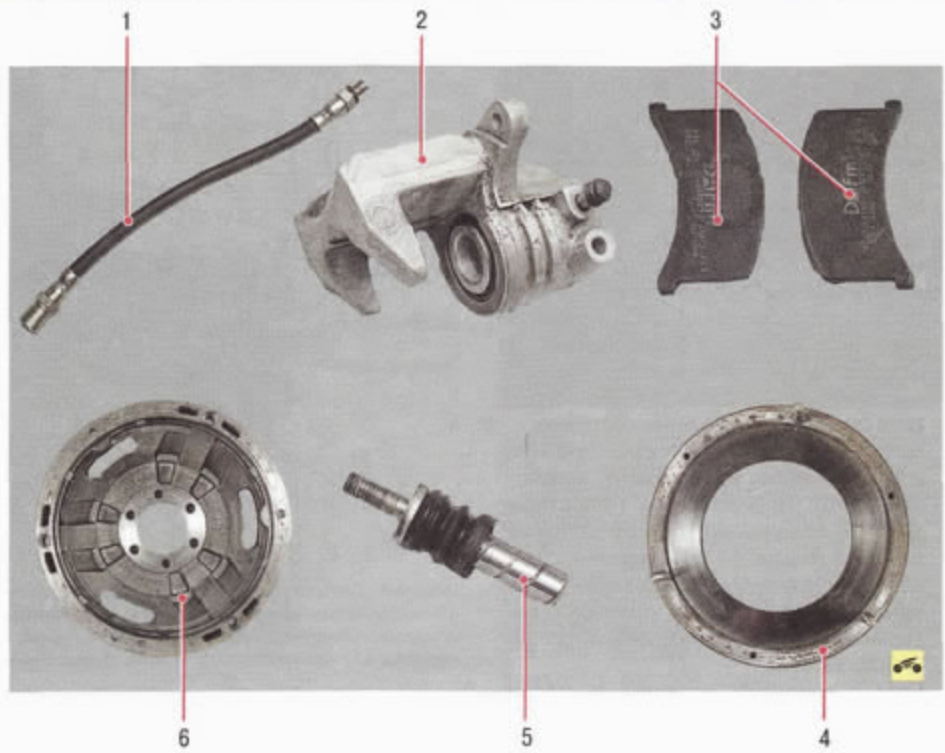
Детали тормозного механизма переднего колеса: 1 — шланг; 2 — суппорт; 3 — тормозные колодки; 4 — тормозной диск; 5 — направляющий палец с защитным чехлом; 6 — фланец ступицы
